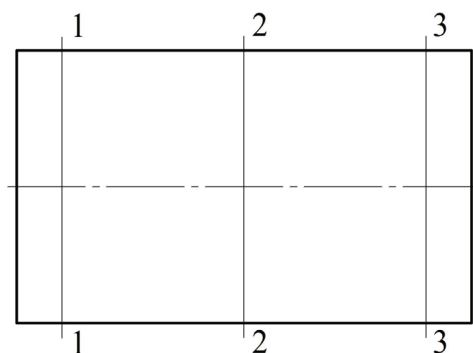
Схема контроля цилиндрической детали калибром-скобой
